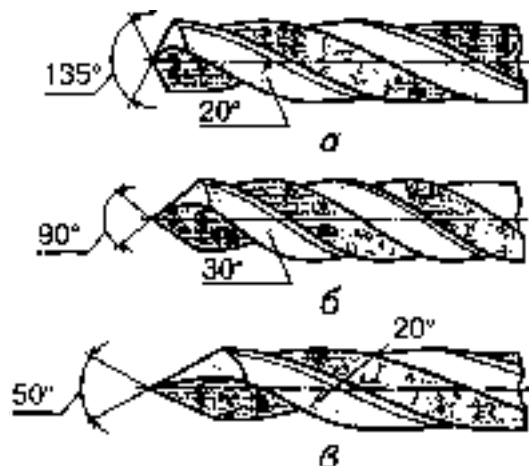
СВЕРДЛА ЗІ СПЕЦІАЛЬНОЮ ЗАТОЧКОЮ ДЛЯ ОБРОБКИ.
